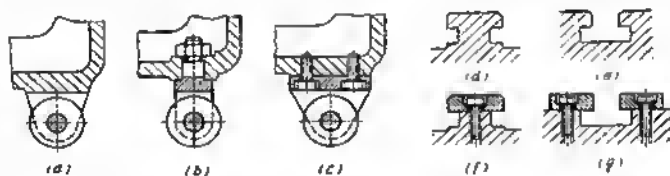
Simplificación del tratamiento mecánico de las piezas tipo armazón, introduciendo piezas separables
